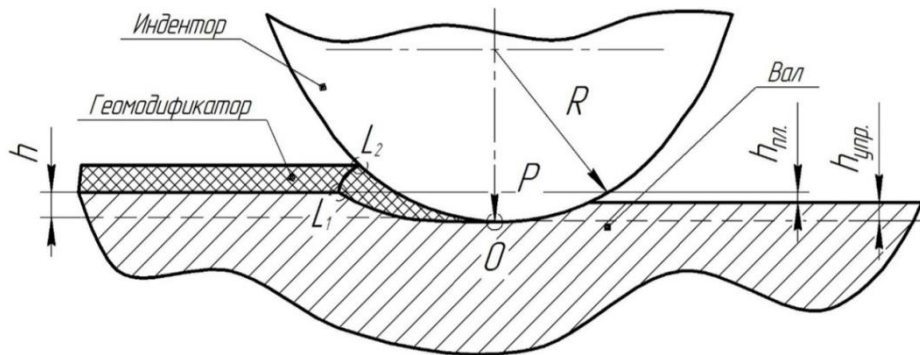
Схема контакта шарового индентора с поверхностью детали при алмазном выглаживании
